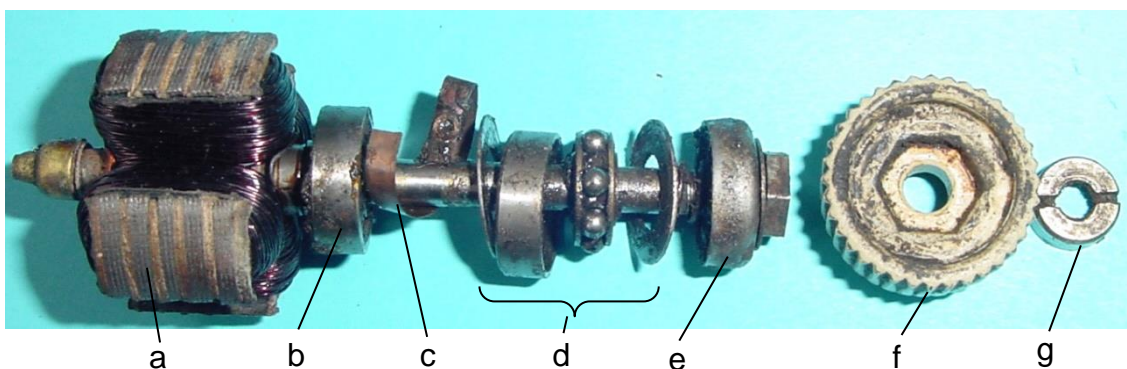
Rotor: a) Anker, b) Unteres Kugellager, c) Massefeder, d) Oberes Kugellager, e) Reibrad, g) Schlitzmutter
